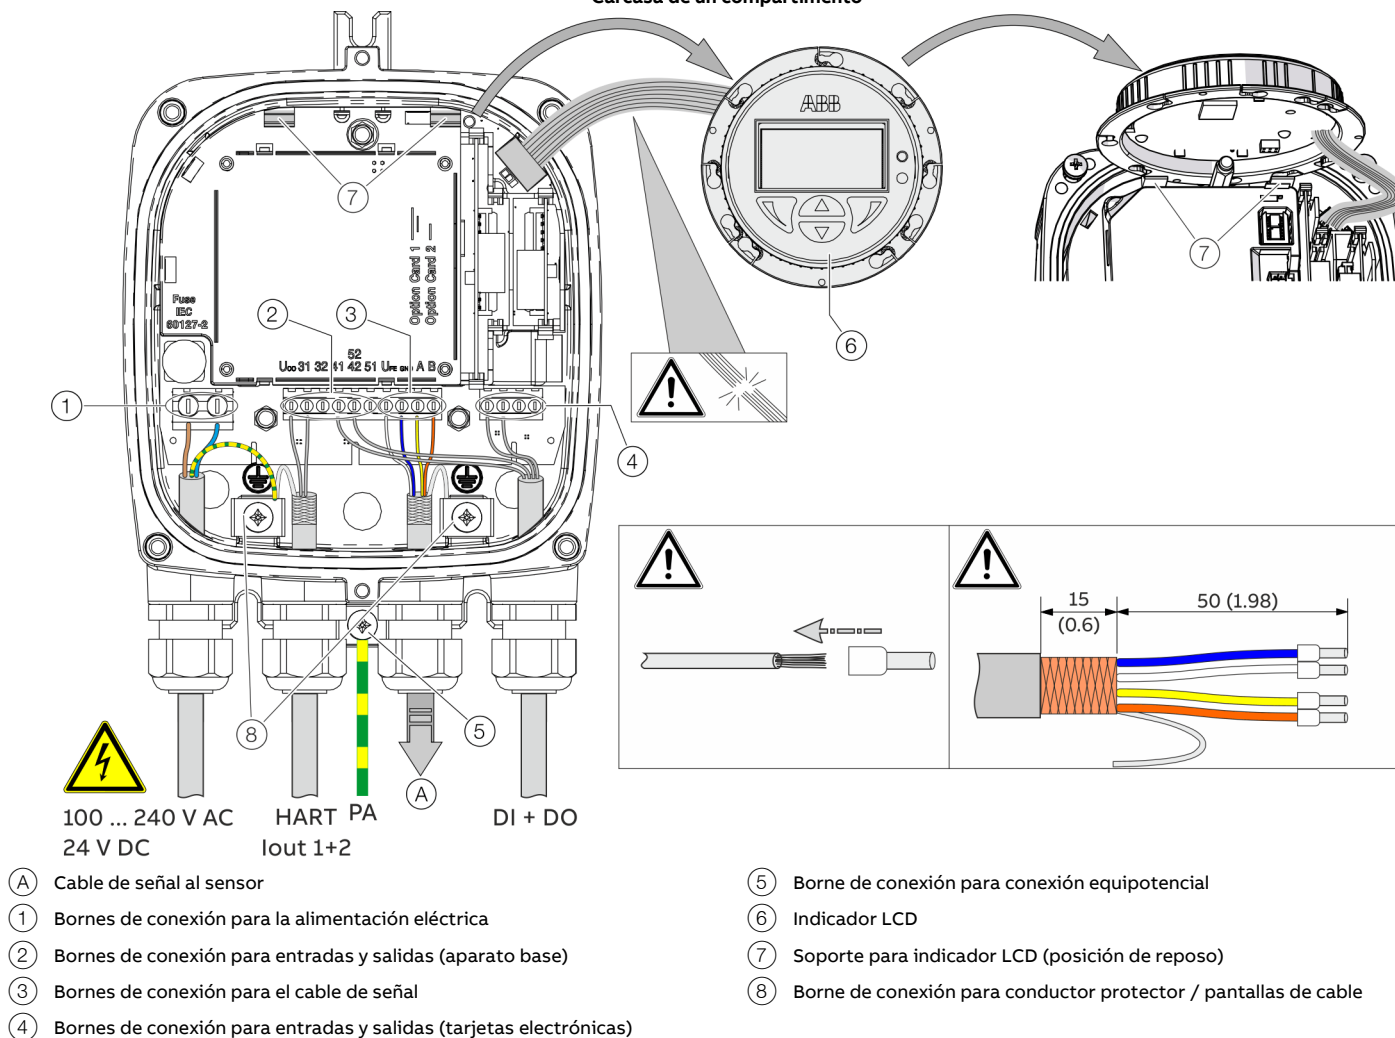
Conexión eléctrica del transmisor en diseño remoto (ejemplo, dimensiones en mm -in-)
